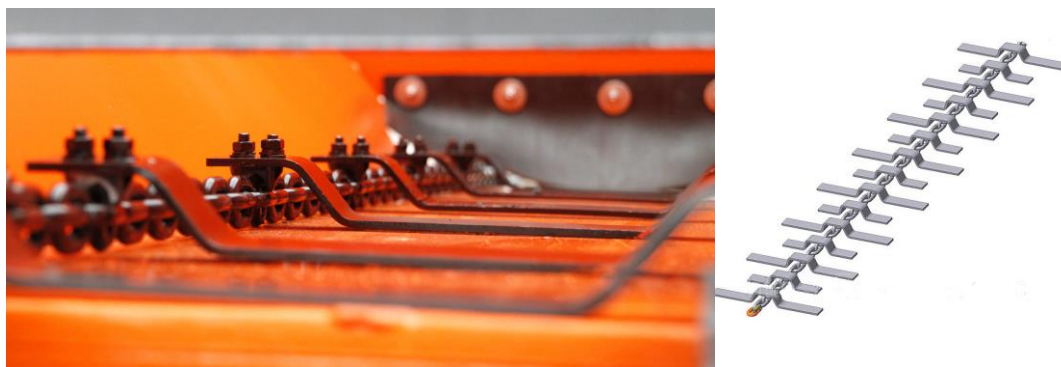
Транспортер пескоразбрасывателя в виде двух втулочно-роликовых цепей
